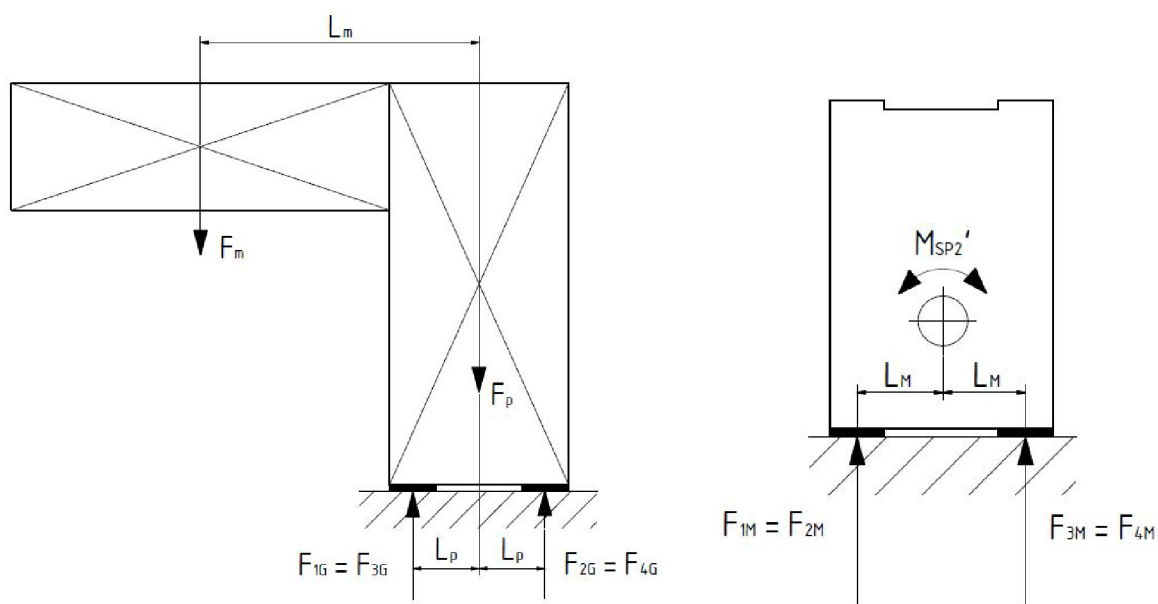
Nahrazení tělesa převodové skříně patkami
